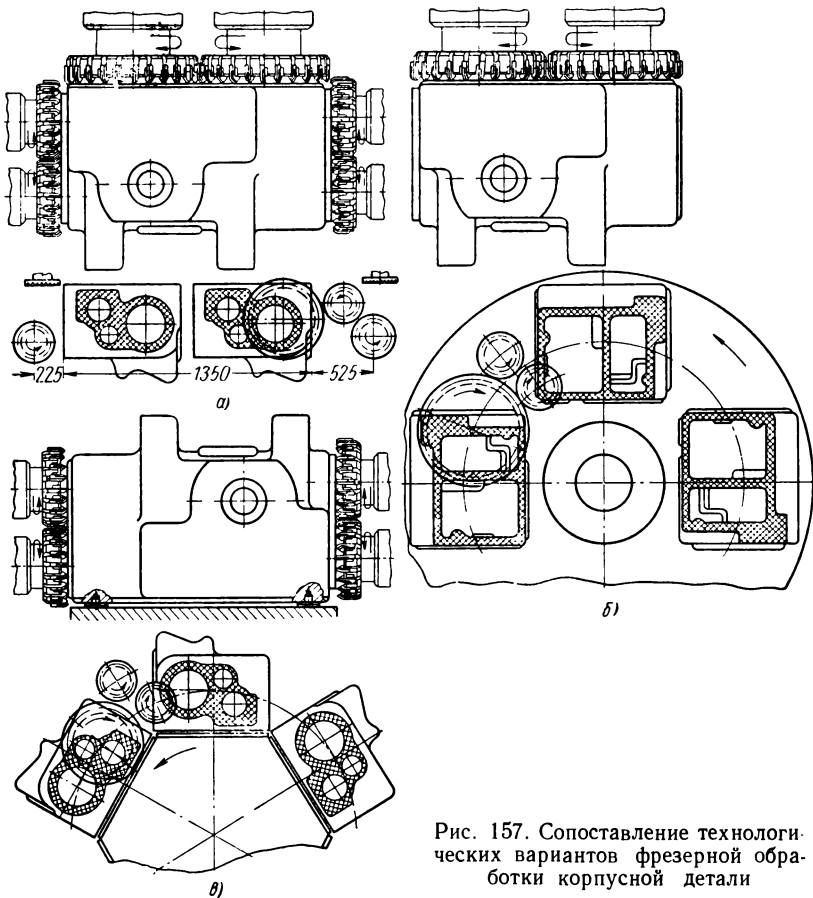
Сопоставление технологических вариантов фрезерной обработки корпусной детали
